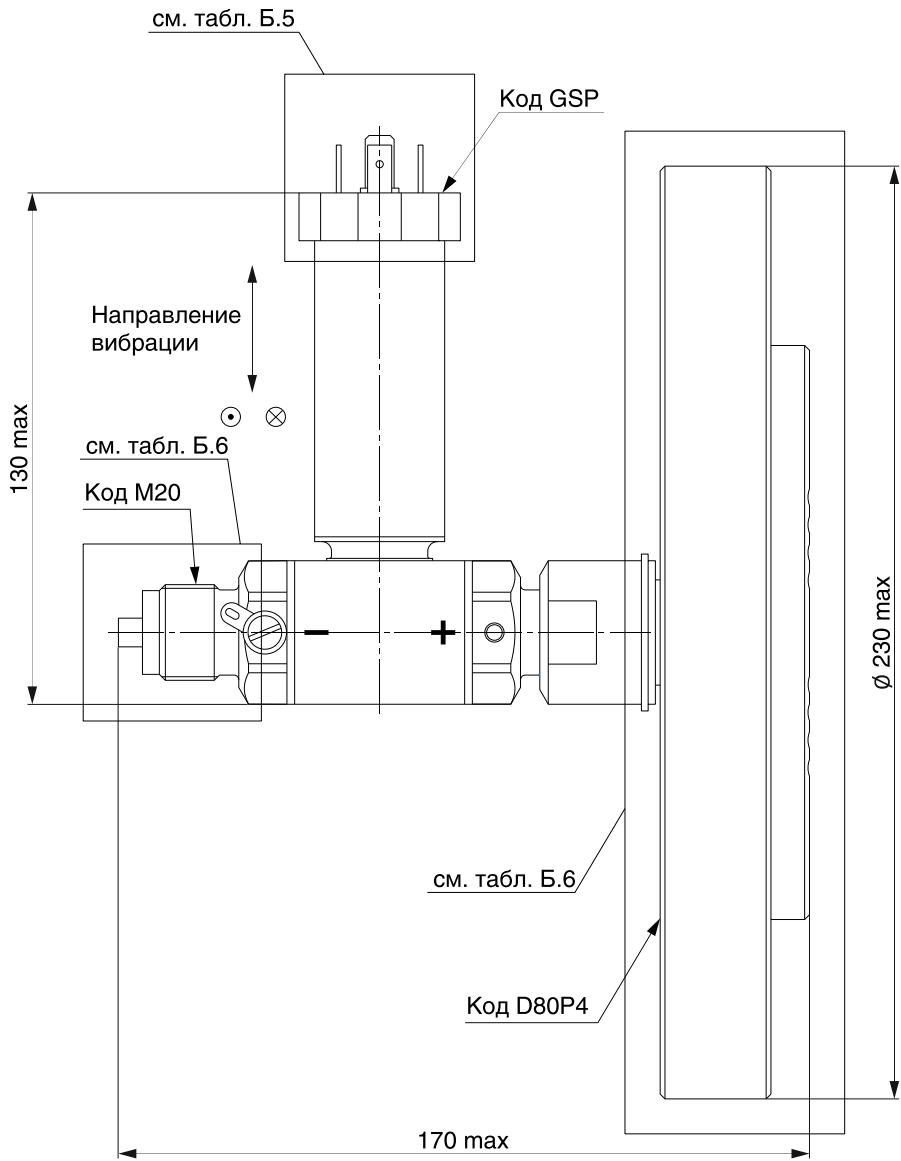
Габаритные и присоединительные размеры датчика
